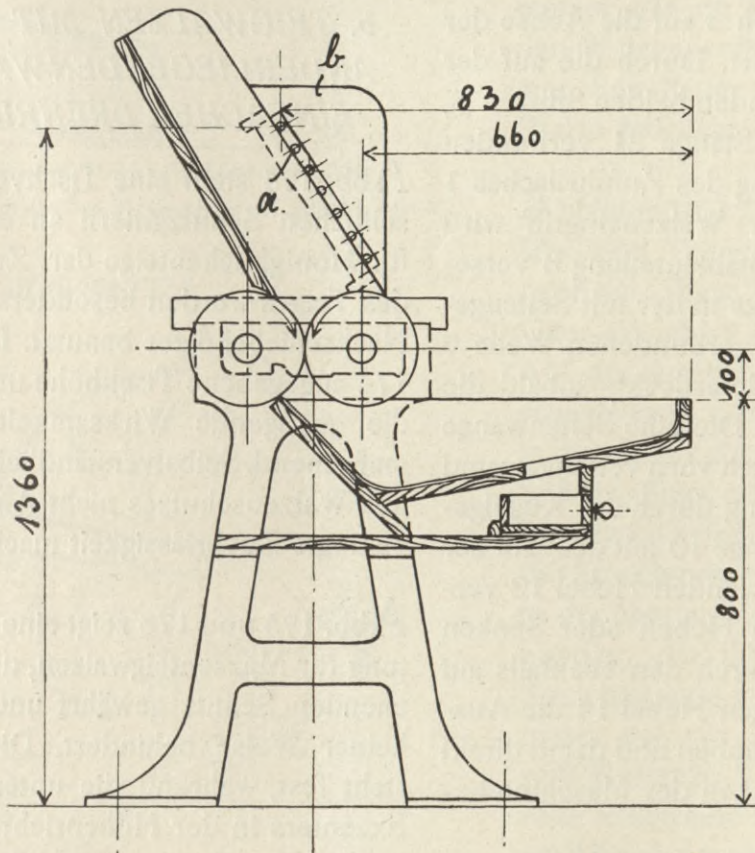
Teigwalze mit nebeneinanderliegendem Walzenpaar der Firma R. Trenk, Erfurt.
